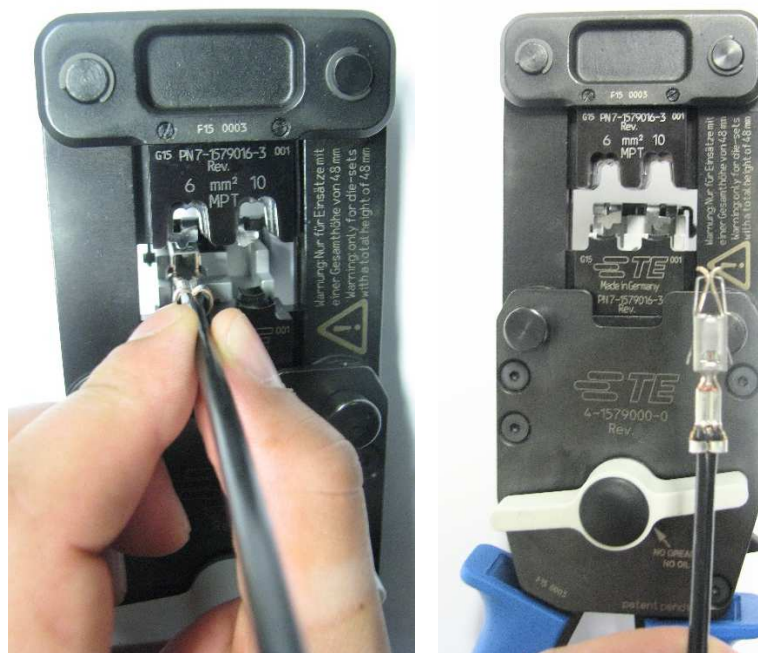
Kontakt entnehmen (links), gecrimpter Kontakt (rechts)
